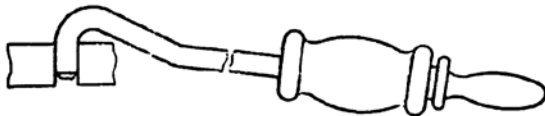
Съемник И801.18.000 крышек коренных опор коленчатого вала
